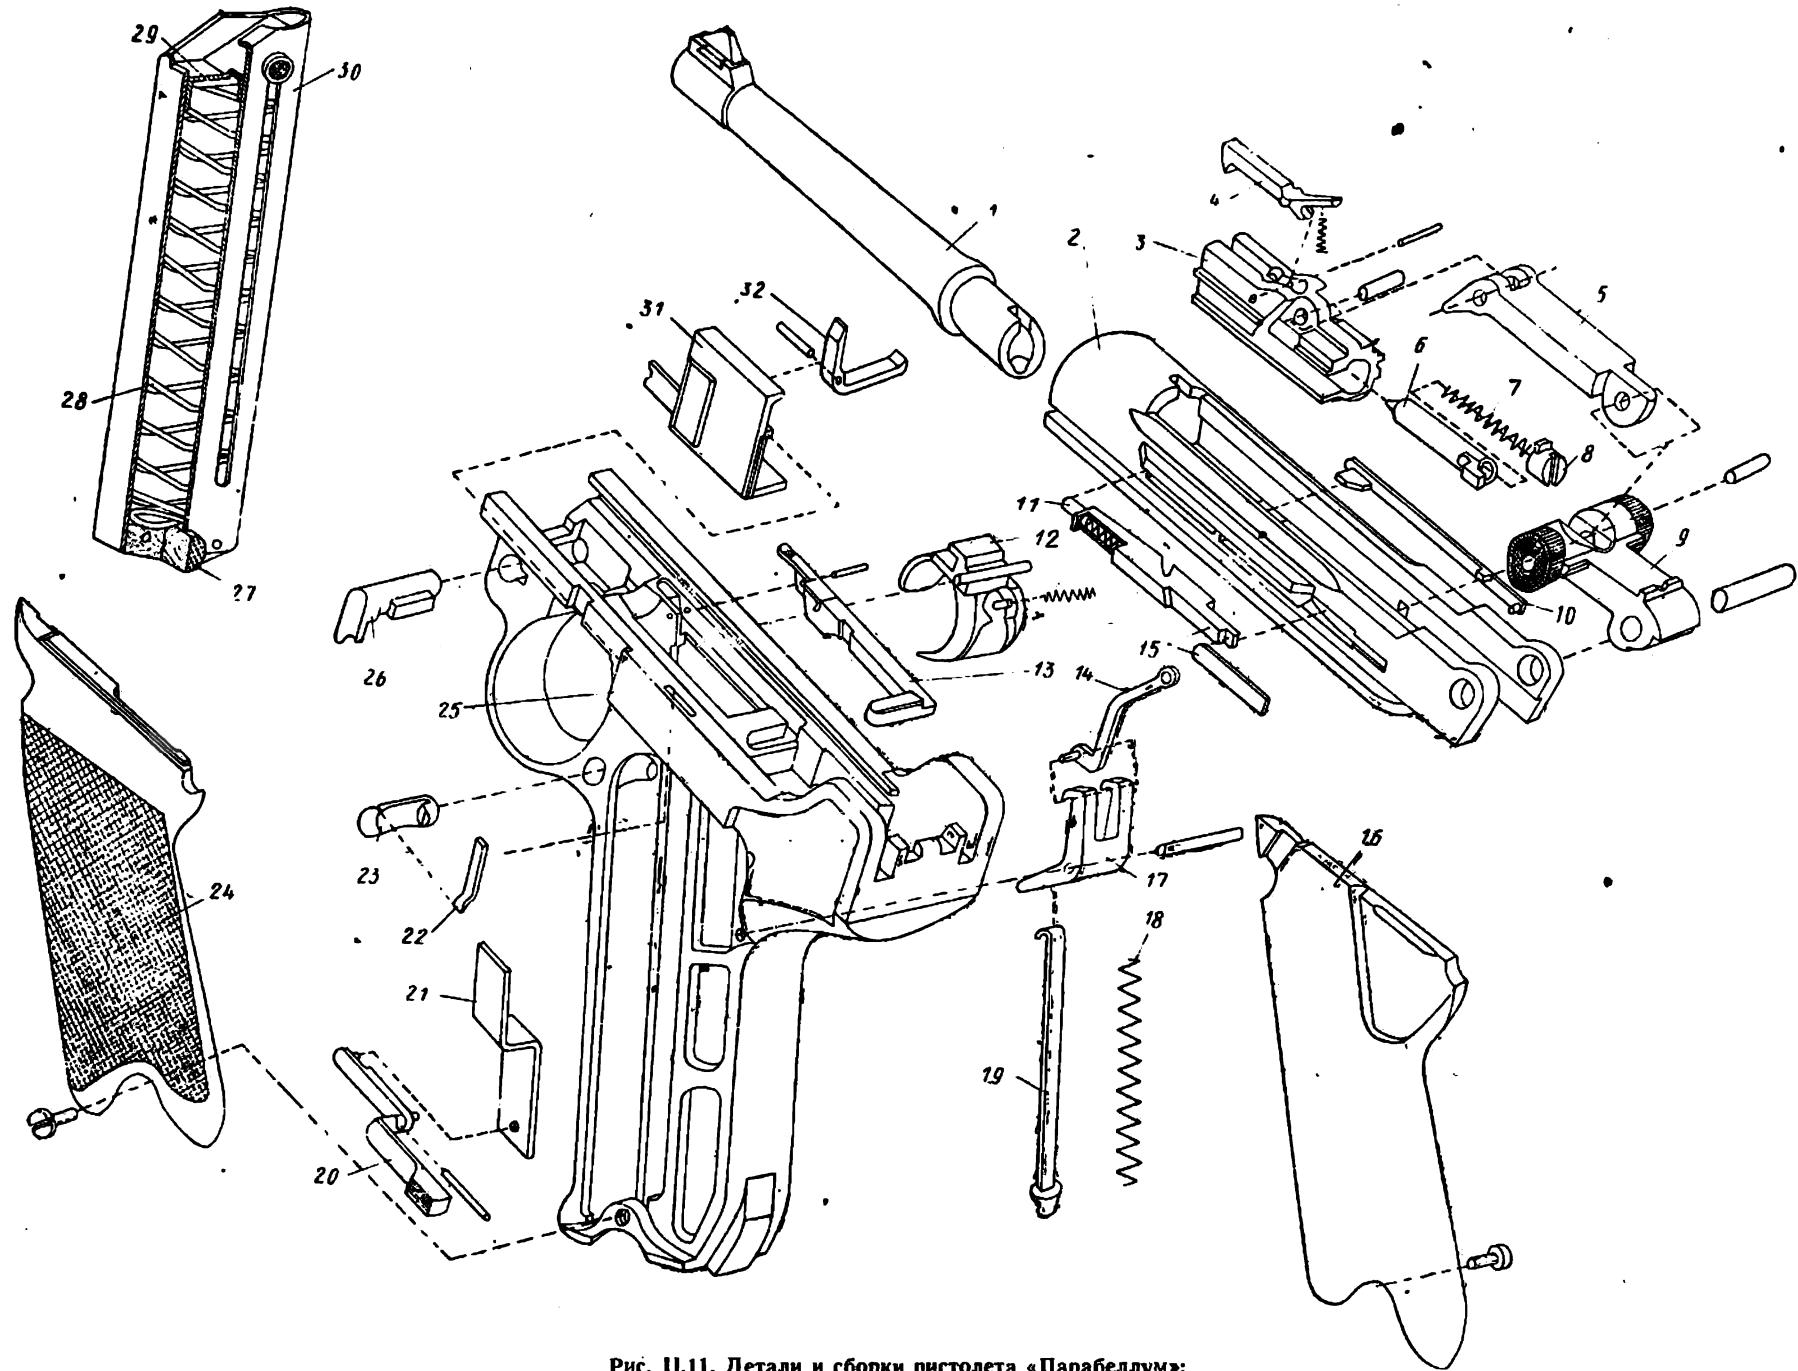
Детали и сборки пистолета «Парабеллум»:
